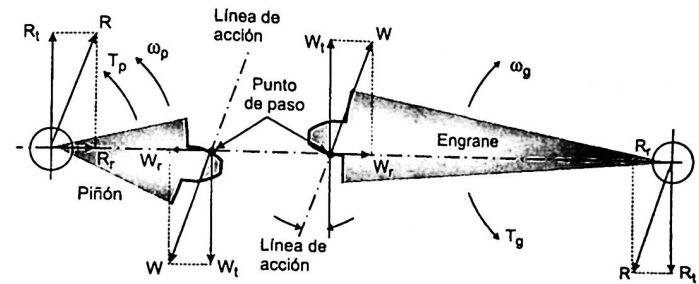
Fuerzas sobre el piñón y el engrane de un engranaje.
